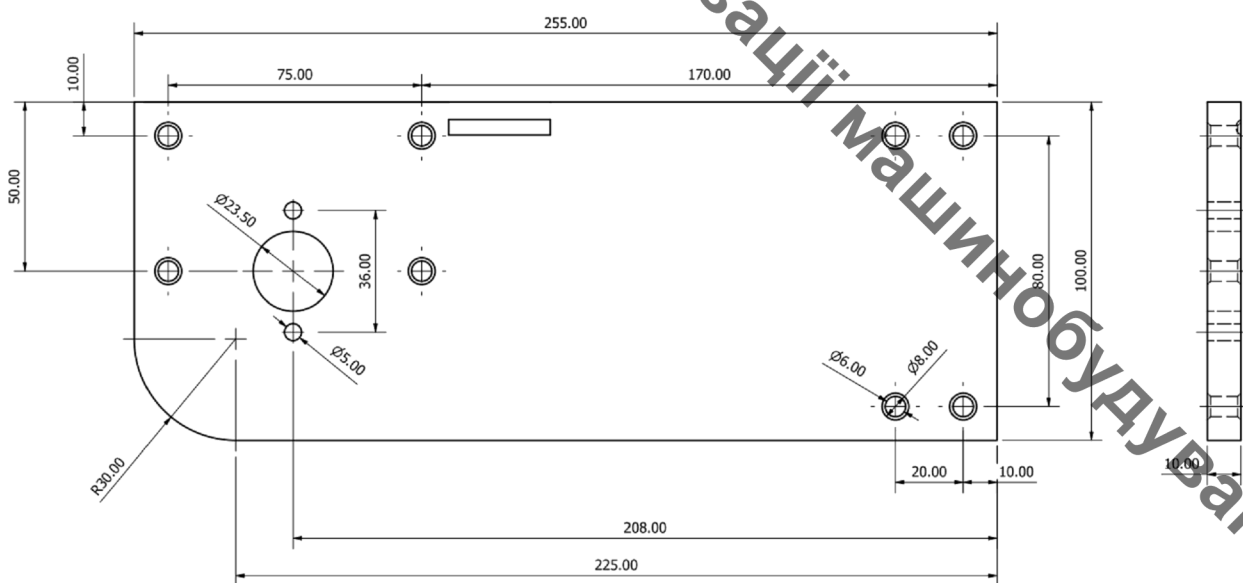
Стойка портала фрезерно-гравірувального верстата з ЧПК моделі CNC 3018-Plus
